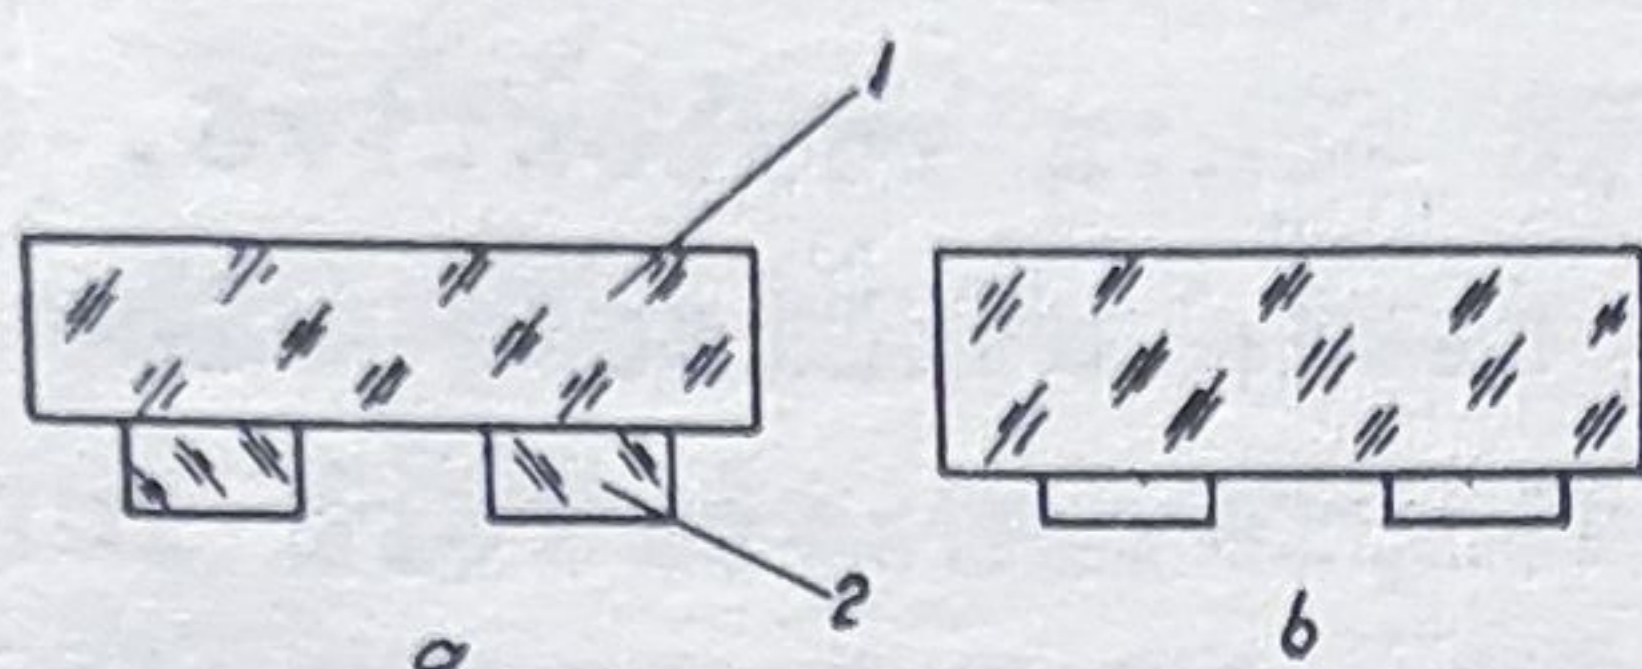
Prelucrarea precisă a lamelor plan-paralele:
